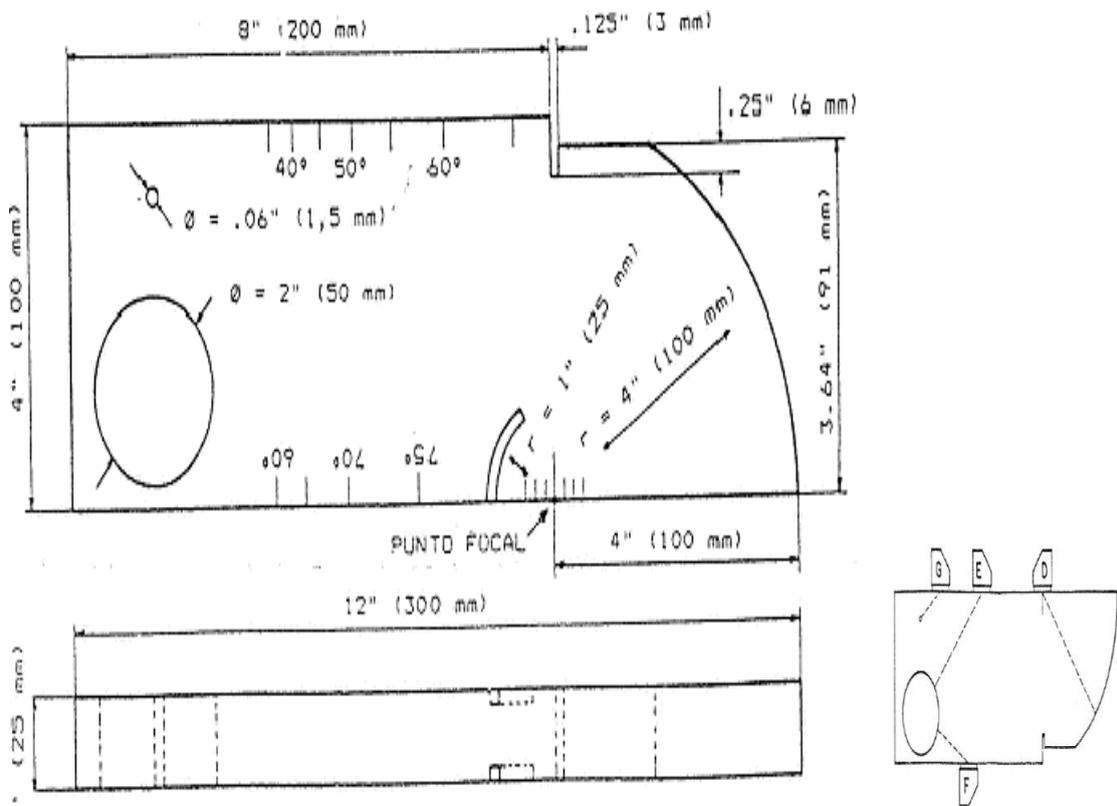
Dimensiones y posiciones de calibración angular, mediante el bloque patrón IIW Tipo 1
